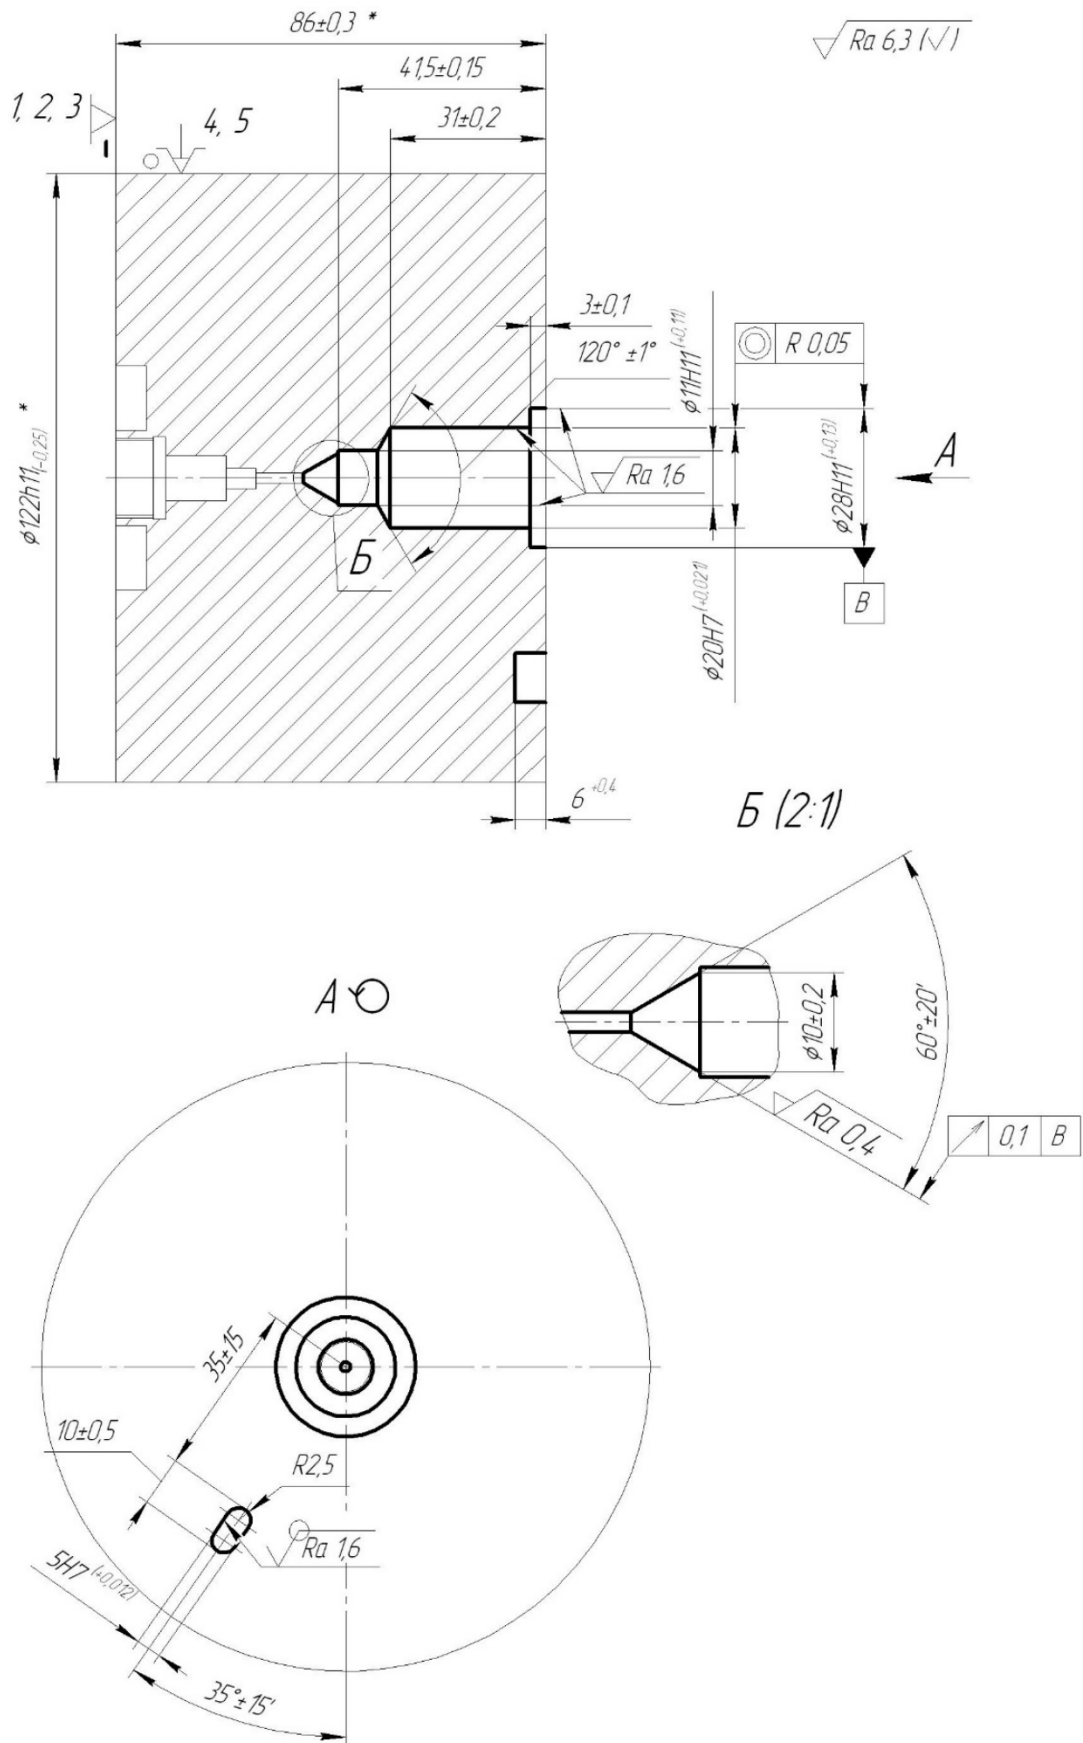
Схема базування та закріплення заготовки на операції 035
